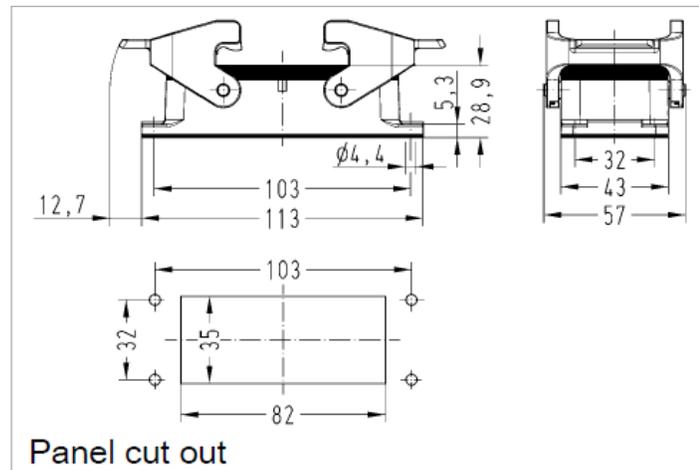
Dimensiones del inserto Harting Han 16 E®
